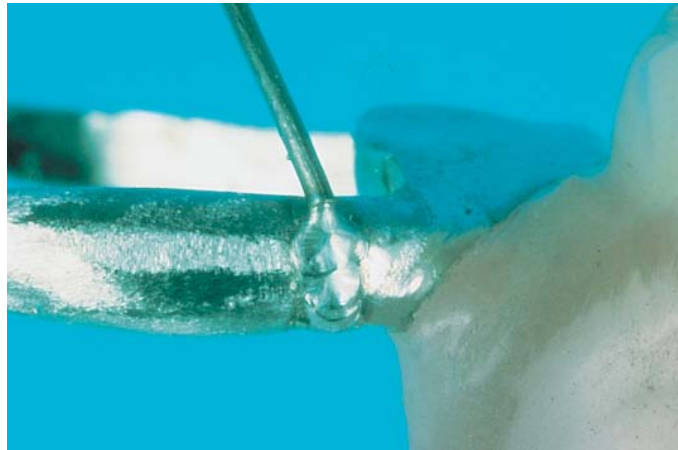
Einbringen von CoCr-Laserschweißdraht
